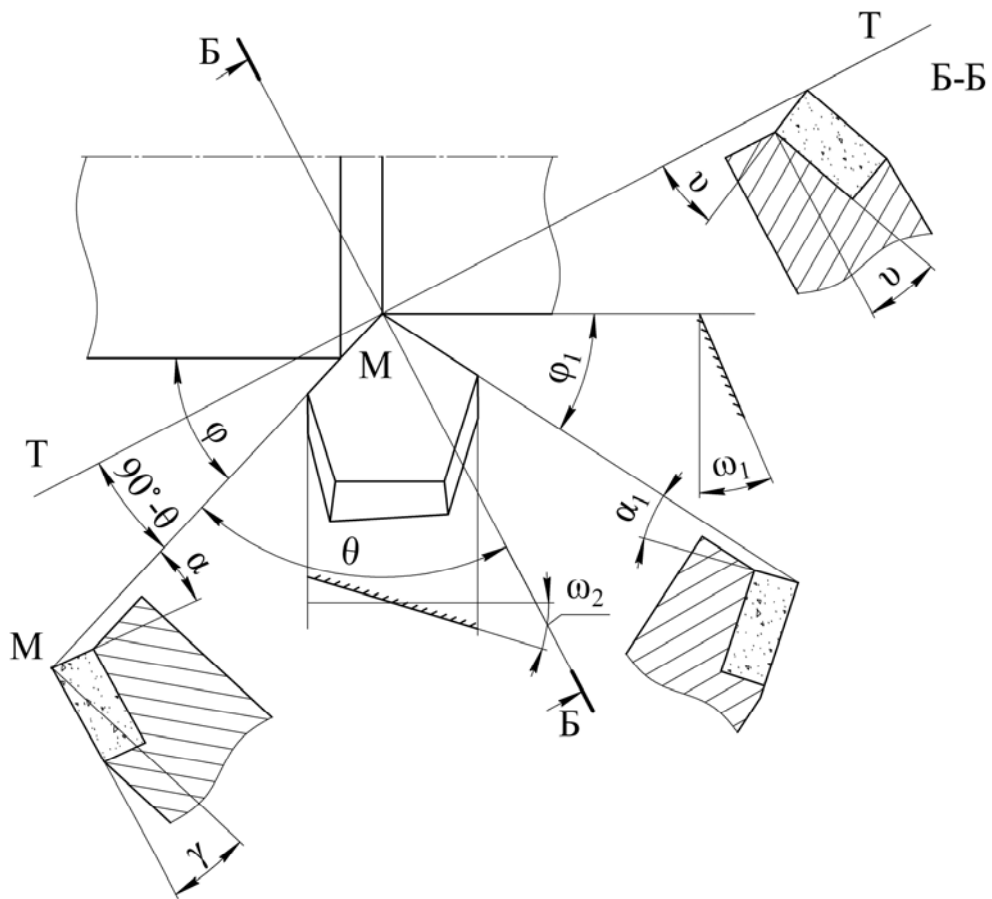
Схема визначення розташування опорної поверхні пластини на корпусі різця
